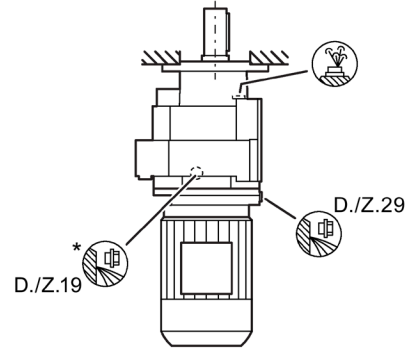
Einbaulagen für Stirnradgetriebe DB/ZB Fuß- / Flanschausführung Baugrößen 39 - 89
